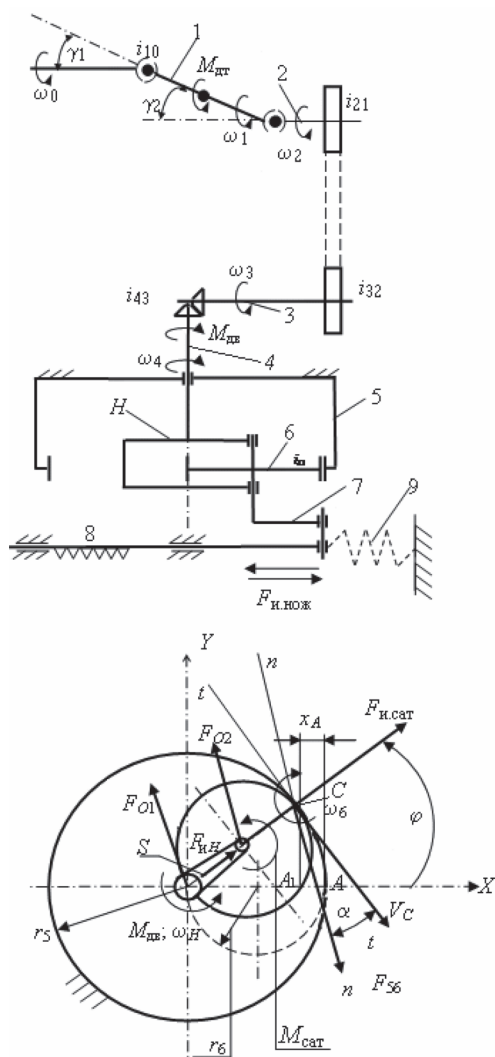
Расчетные схемы для кинестатического расчета привода жатки с планетарным механизмом: 1, 2 – валы карданной передачи; 3 – вал ременной передачи; 4 – входной вал планетарного механизма; 5 – центральное зубчатое колесо планетарного механизма; 6 – сателлит; H – водило; 7 – кривошип; 8 – нож режущего аппарата жатки; 9 – упругость рекуператора
